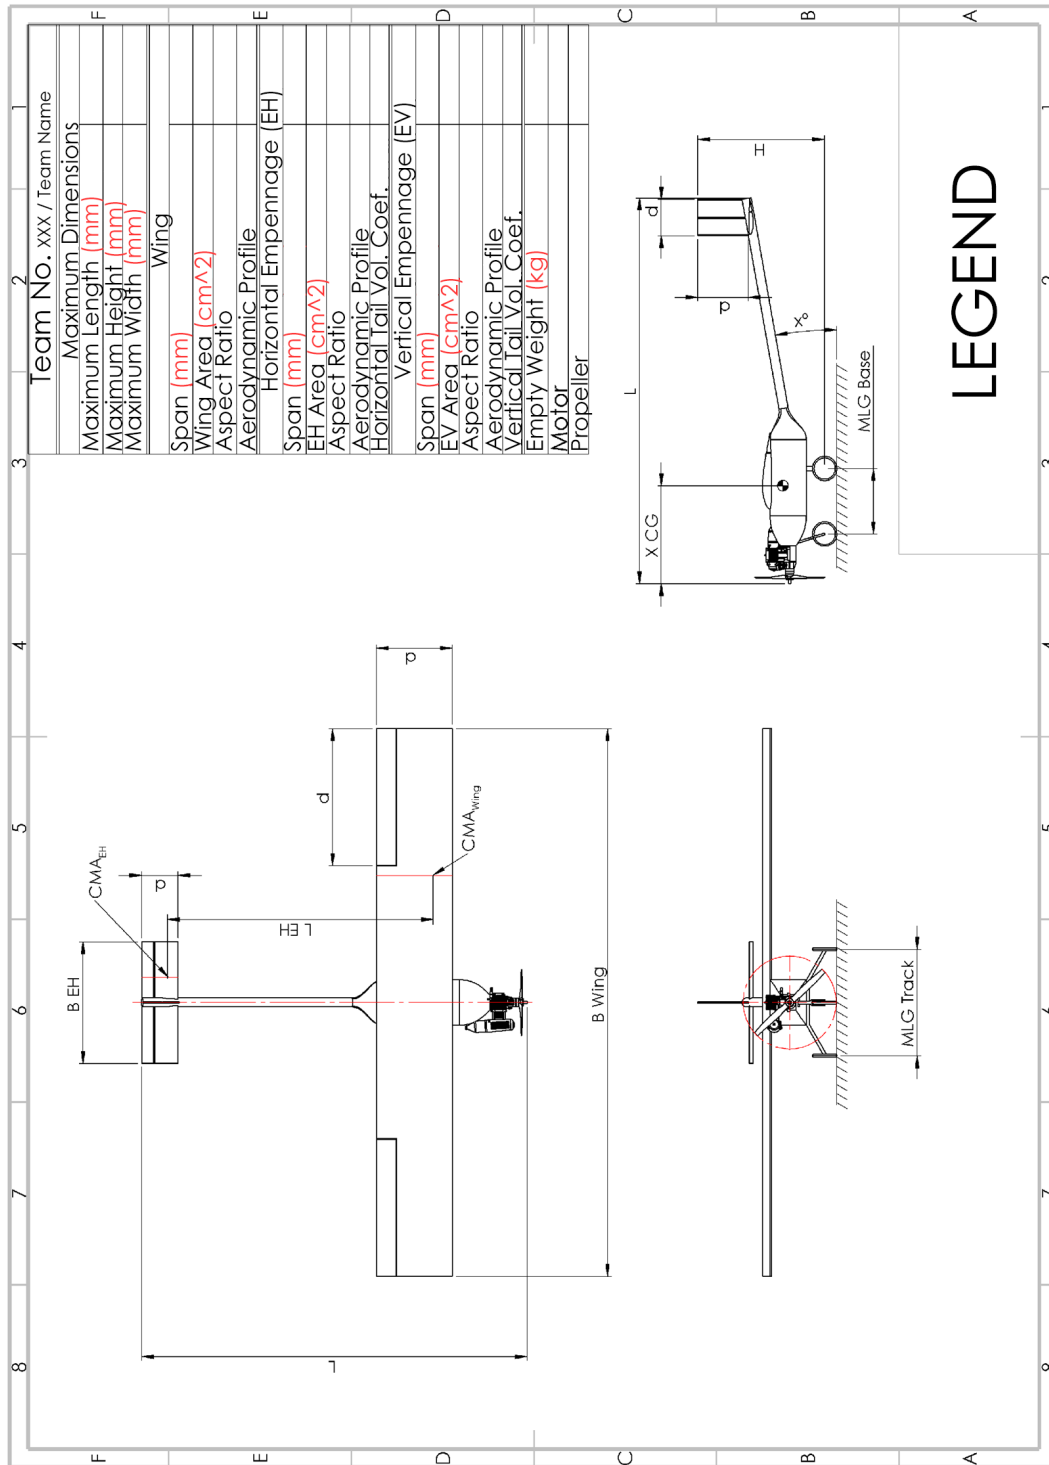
Example of a Three-View Drawing. Use dimensions in the International System.
